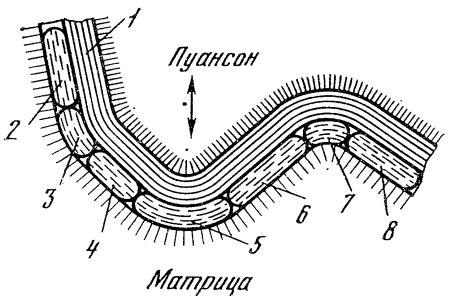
Схема склеивания гнутоклеенных заготовок из шпона методом эластичной передачи давления:
